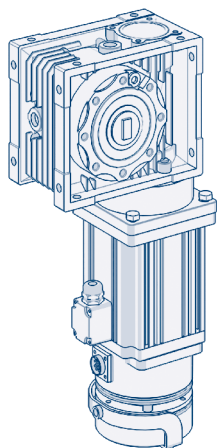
Порядок установки рычага расцепителя тормоза
